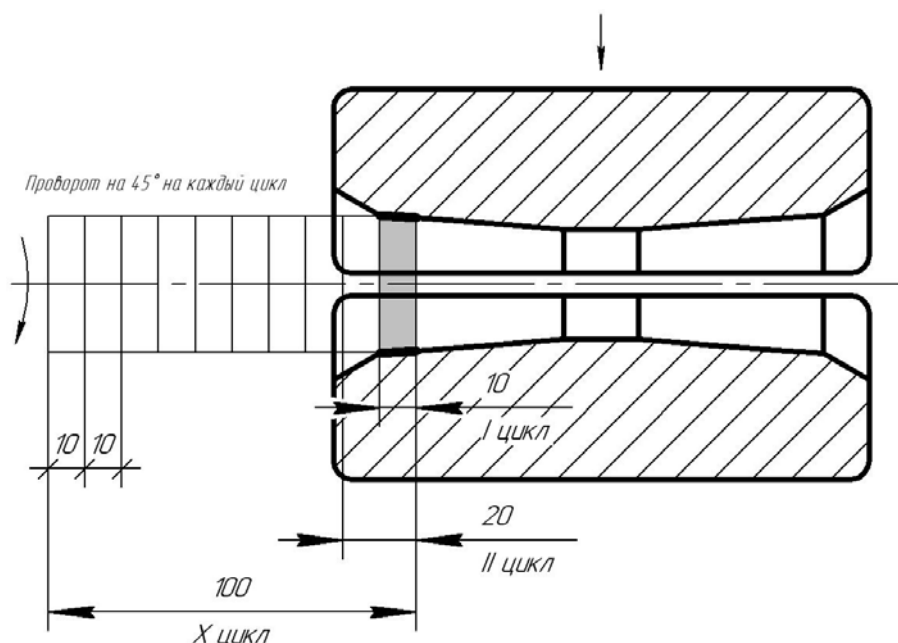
Схема обжатия заготовки, заготовка изображена в момент I цикла
